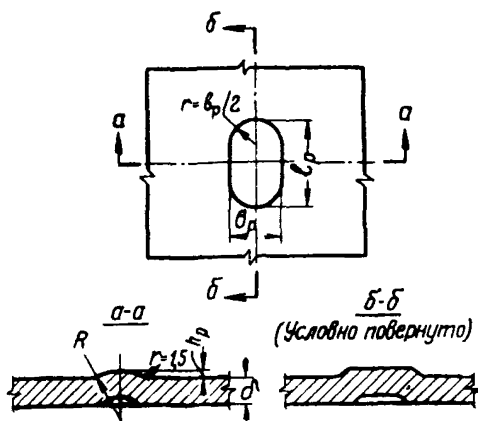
Размеры рельефа в плоском элементе, подготовленном к сварке нахлесточного соединения элементов закладной детали
